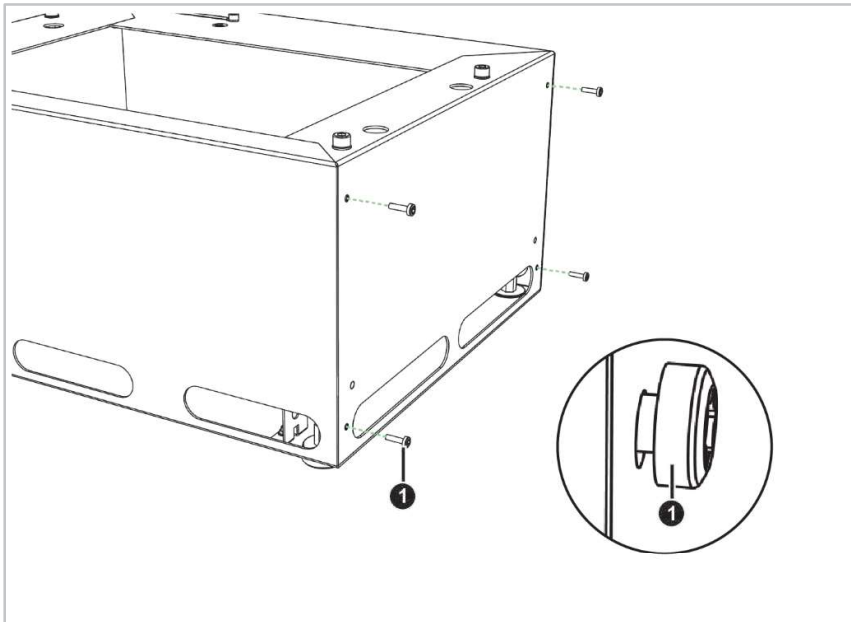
Linsenkopfschrauben in Sockel einschrauben (Abbildung ohne Funktionseinheit/Batterieschrank)
